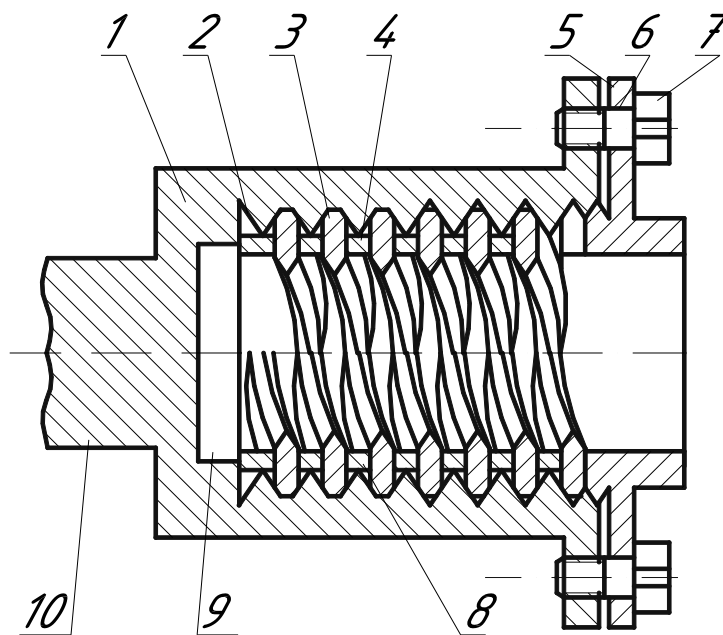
Пристрій для нарізання різі у НГД
